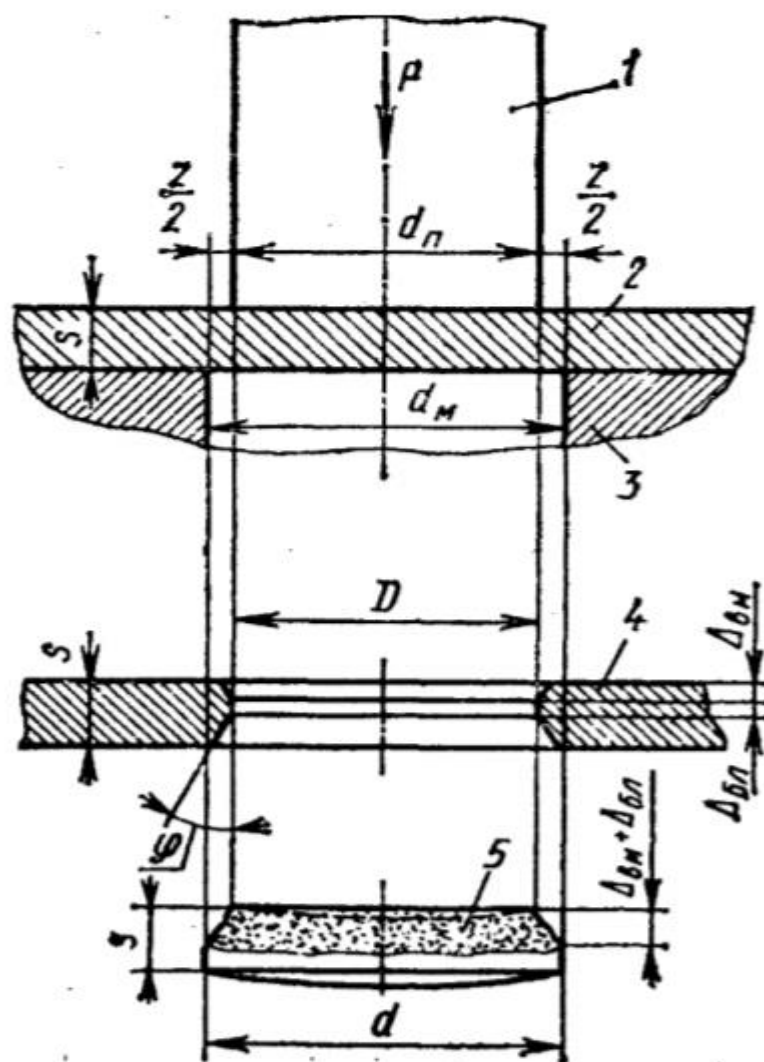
Схема пробивки-вырубki и погрешности деталей после штамповки: 1 – пуансон; 2 – заготовка; 3 – матрица; 4 – заготовка с пробитым отверстием; 5 – вырубленная деталь ($\Delta_{\text{вм}}$ - глубина вмятины, образующейся в начальный момент пробивки-вырубki; $\Delta_{\text{бл}}$ - высота блестящего пояска; φ - угол скола)
